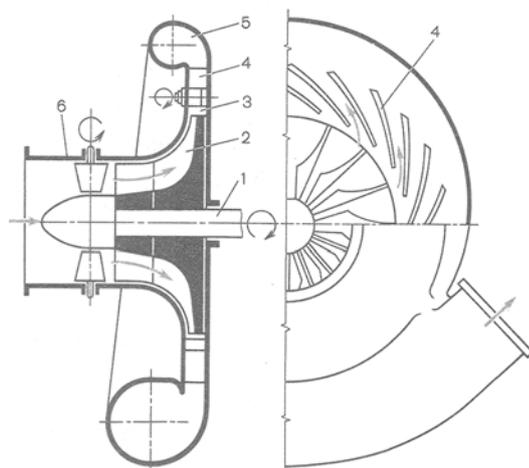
Принципиальная схема одноступенчатого центробежного компрессора: 1 – гладкий вал; 2 – рабочее колесо; 3 – диффузор; 4 – лопатки; 5 – воздухосборник; 6 – входное устройство
